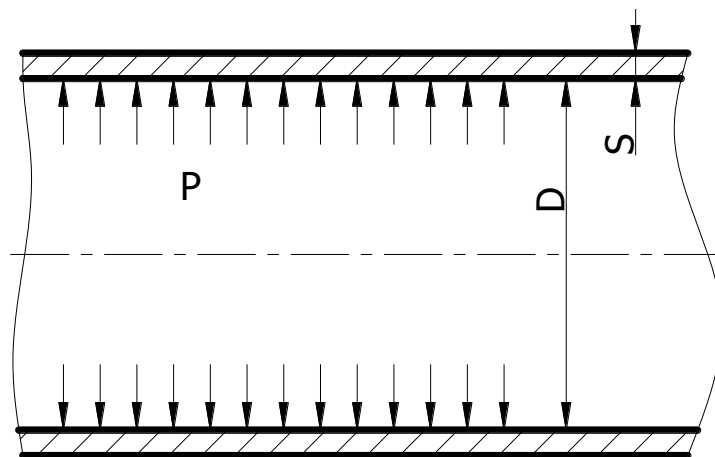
Розрахункова схема циліндричної обичайки
